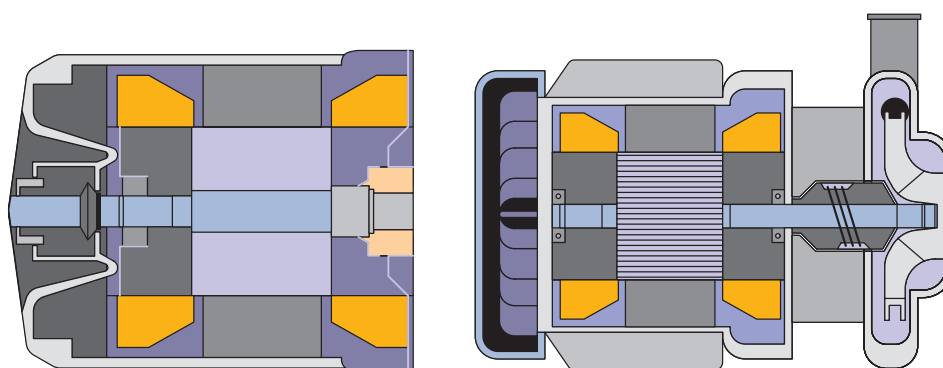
Pompe à rotor noyé, à gauche, et à moteur ventilé, à droite. Vue en coupe.
